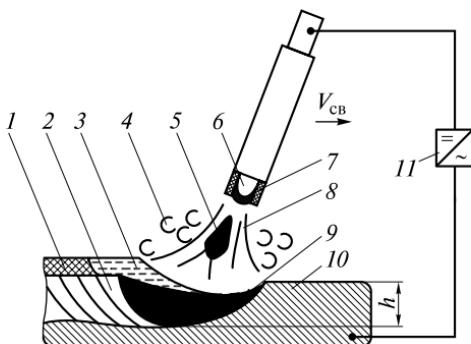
Схема ручной дуговой сварки покрытым электродом:
